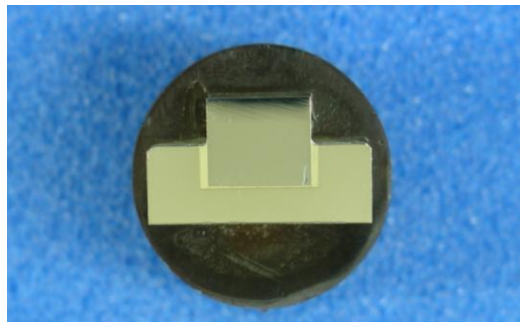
Disposición de las probetas seccionadas en el ensayo de cizalla.
